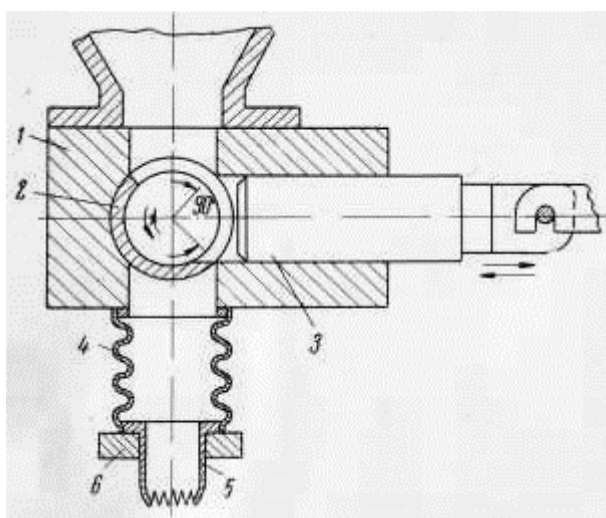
Схема дозувально-відсадочного механізму
